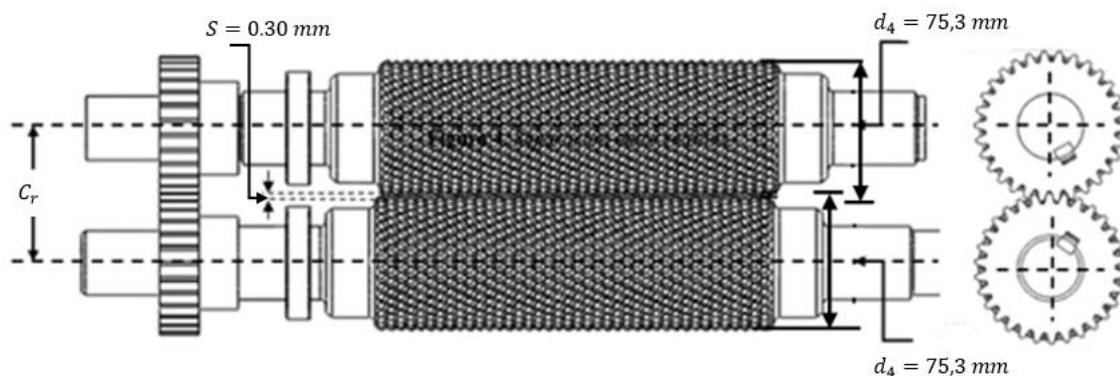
Separación del rodillo para seleccionar el diámetro del engranaje.
